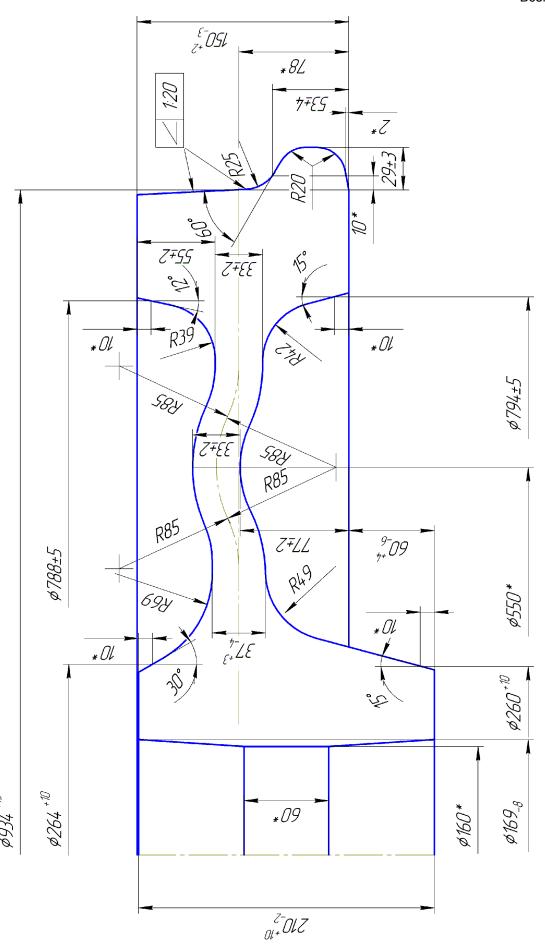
Колесо без механической обработки \varnothing 934 мм под \varnothing 920 мм, черт. В.03.02.02.01 . Масса чернового колеса на 2/3 поля допуска = 497 кг.
